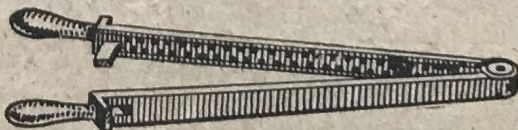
Moule pour fabriquer dragée coulée au moule.
